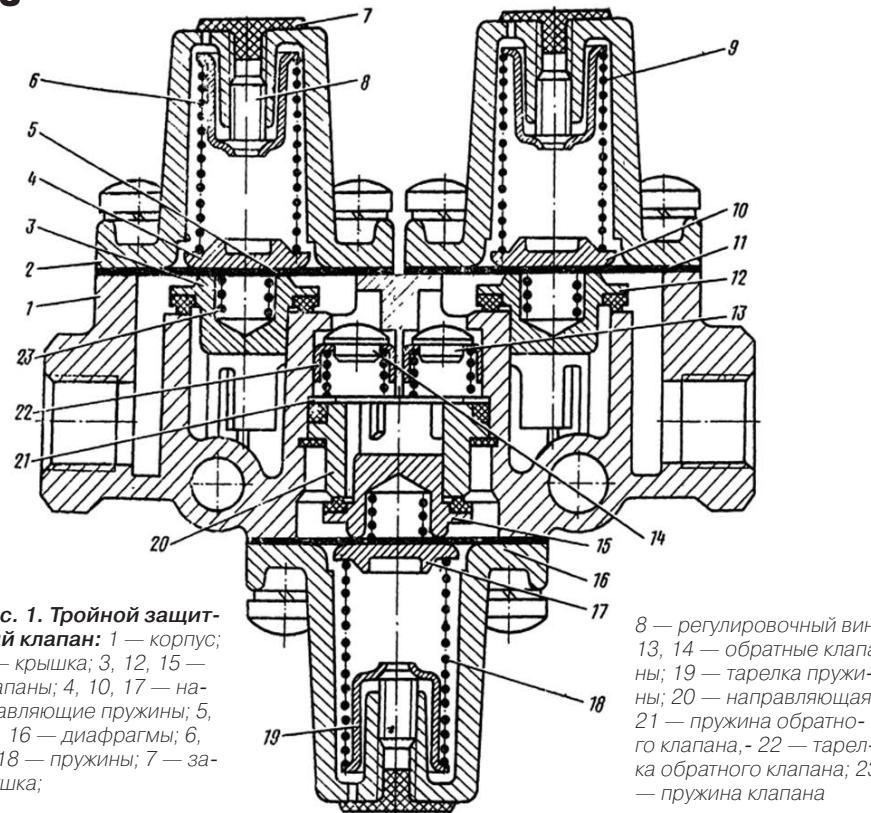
Тройной защитный клапан: 1 — корпус; 2 — крышка; 3, 12, 15 — клапаны; 4, 10, 17 — направляющие пружины; 5, 11, 16 — диафрагмы; 6, 9, 18 — пружины; 7 — заглушка;
